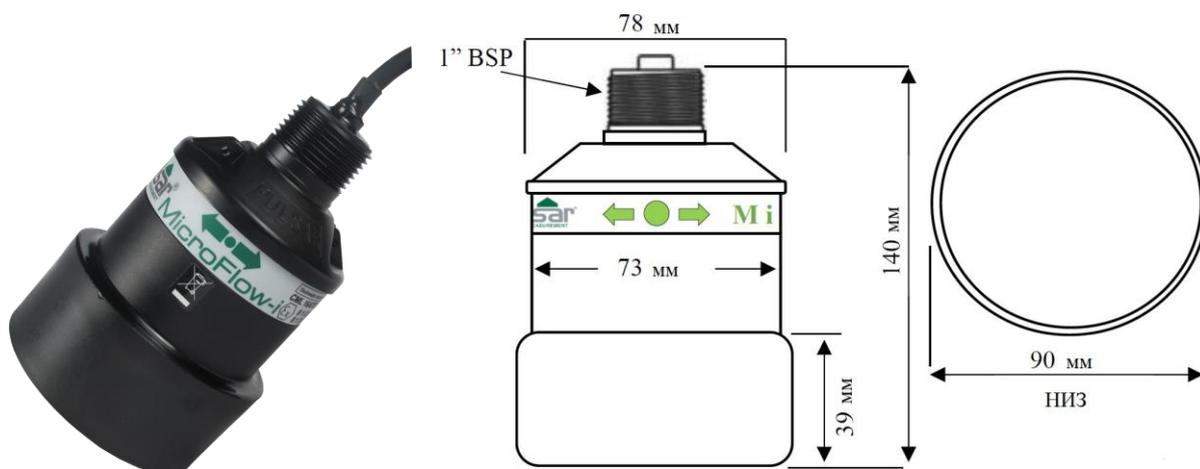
Внешний вид и габаритные размеры радарного датчика скорости
